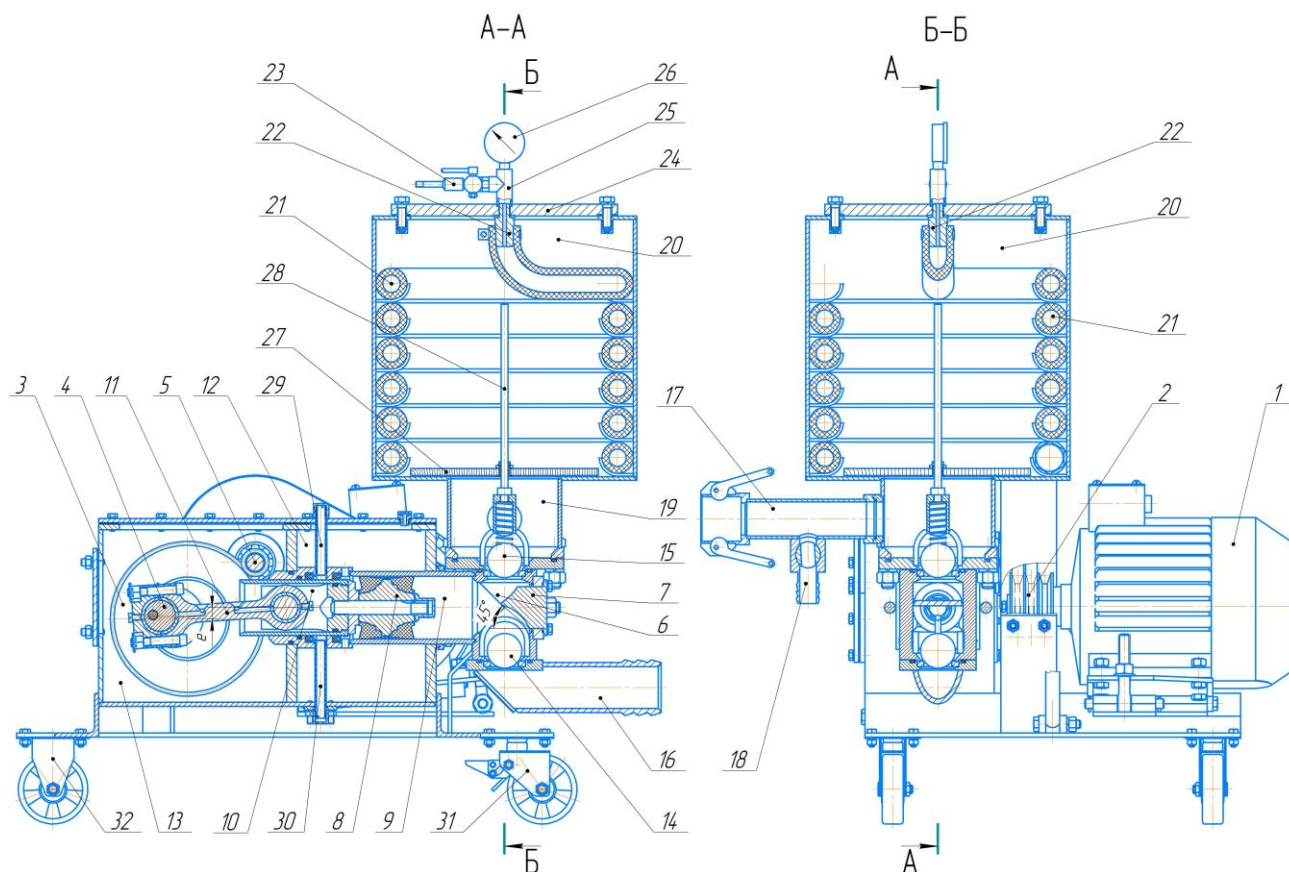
Однопоршневий розчинонасос з комбінованим компенсатором збільшеного об'єму: 1 – електродвигун; 2 – клинопасова передача; 3 – зубчасте колесо; 4 – кривошипний вал; 5 – вал-шестерня; 6 – всмоктувальна камера; 7 – спеціальна циліндрична вставка; 8 – поршень; 9 – робочий циліндр; 10 – повзун; 11 – шатун; 12 – камера; 13 – корпус редуктора; 14, 15 – всмоктувальний та нагнітальний підпружинений кульові клапани; 16, 17 – всмоктувальний і нагнітальний патрубки; 18 – кран зниження тиску; 19 – нагнітальна камера; 20 – циліндрична камера; 21 – замкнена камера; 22 – штуцер вузла підкачки повітря; 23 – ніпель; 24 – кришка; 25 – кран; 26 – манометр; 27 – поплавков-обмежувач; 28 – направляючий стрижень; 29, 30 – каналні патрубки; 31, 32 – пара коліс.
